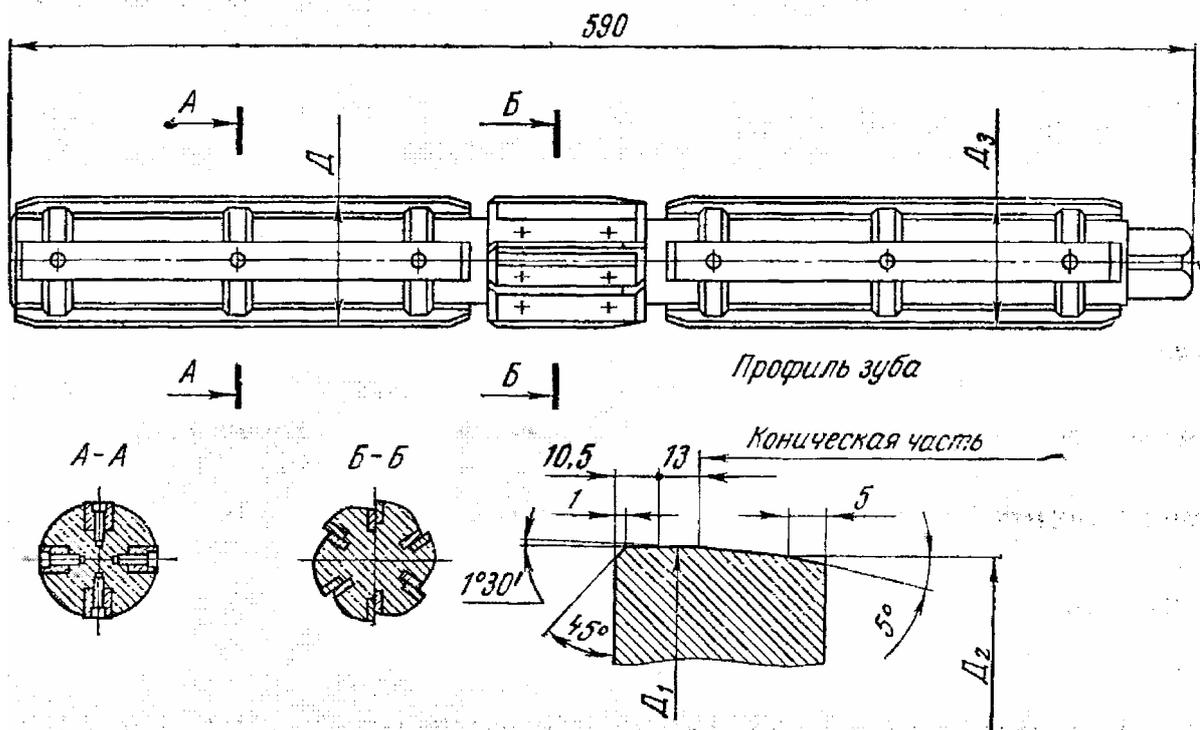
Развертка для обработки отверстий втулок под шейки распределительного вала
